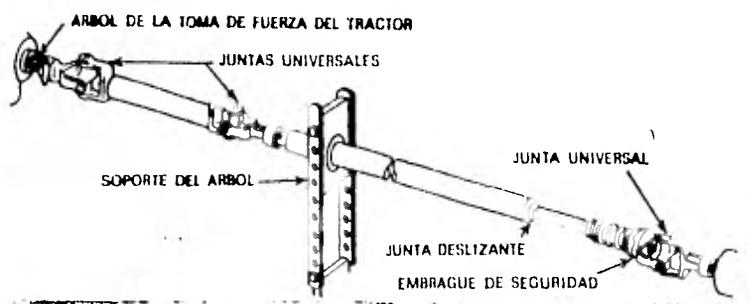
Conjunto de toma de fuerza con tres juntas universales, soporte del árbol y embrague de seguridad.
